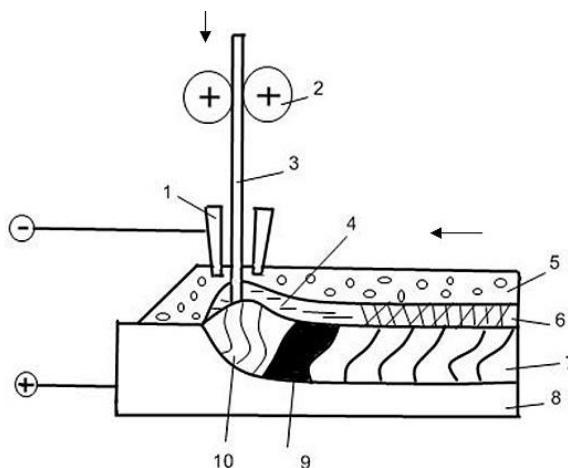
Схема однодугового зварювання під флюсом: 1 – струмопідвід, 2 – механізм подачі дроту, 3 – дріт, 4 – рідкий шлак, 5 – флюс, 6 – шлакова кірка, 7 – зварний шов, 8 – основний метал, 9 – зварювальна ванна, 10 – електрична дуга
